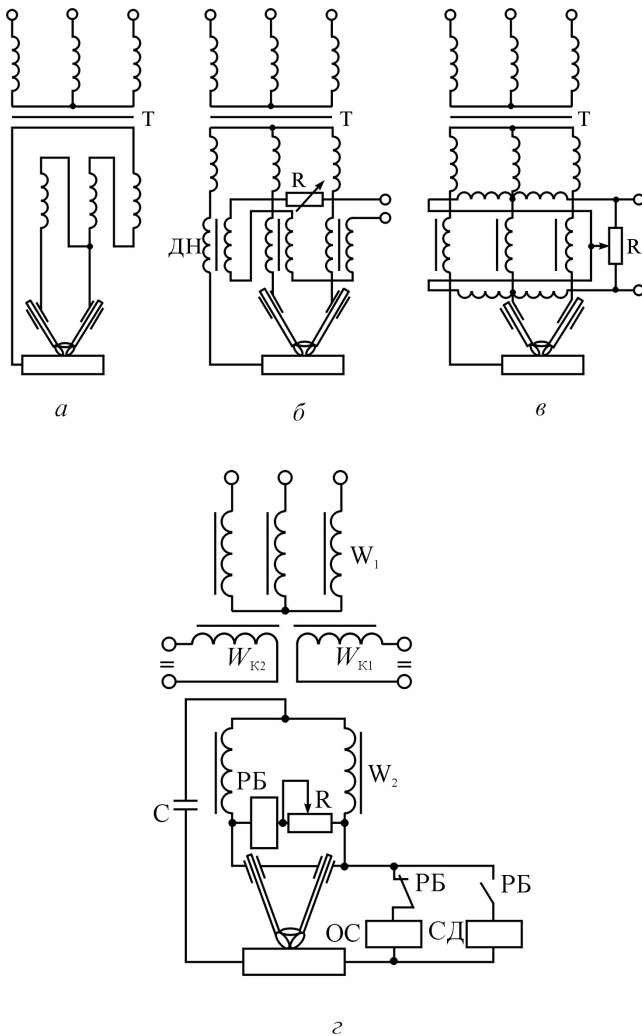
Схеми джерел живлення для зварювання трифазною дугою
